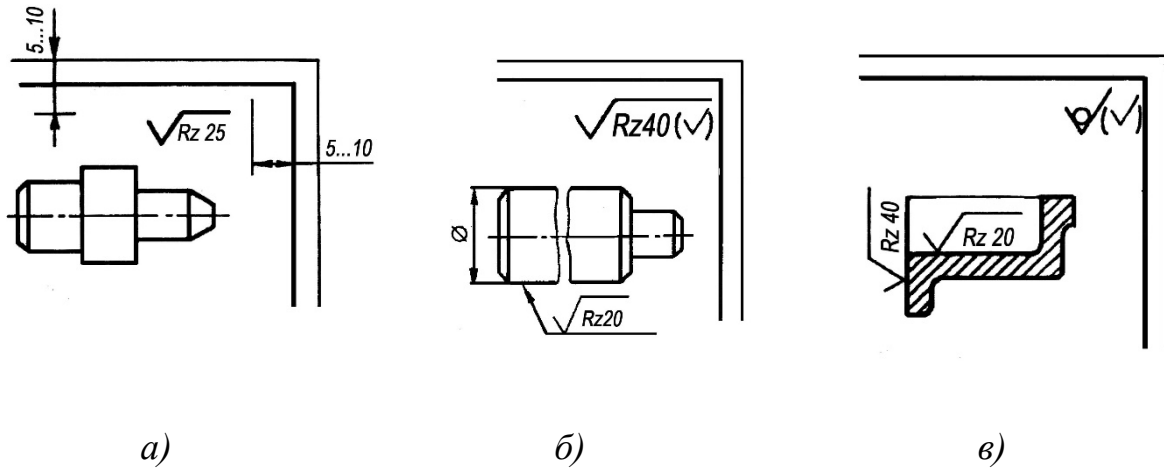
Обозначение одинаковой (а) и преобладающей (б, в) шероховатости
